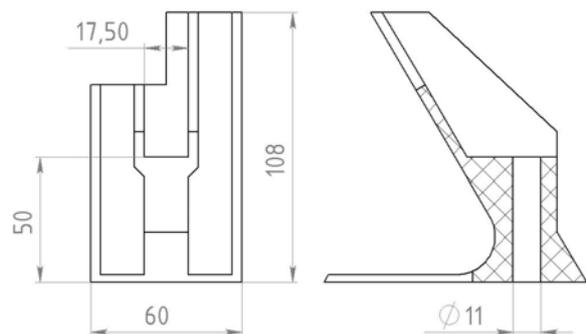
Внешний вид и габаритные размеры УКК-60 (мм)
